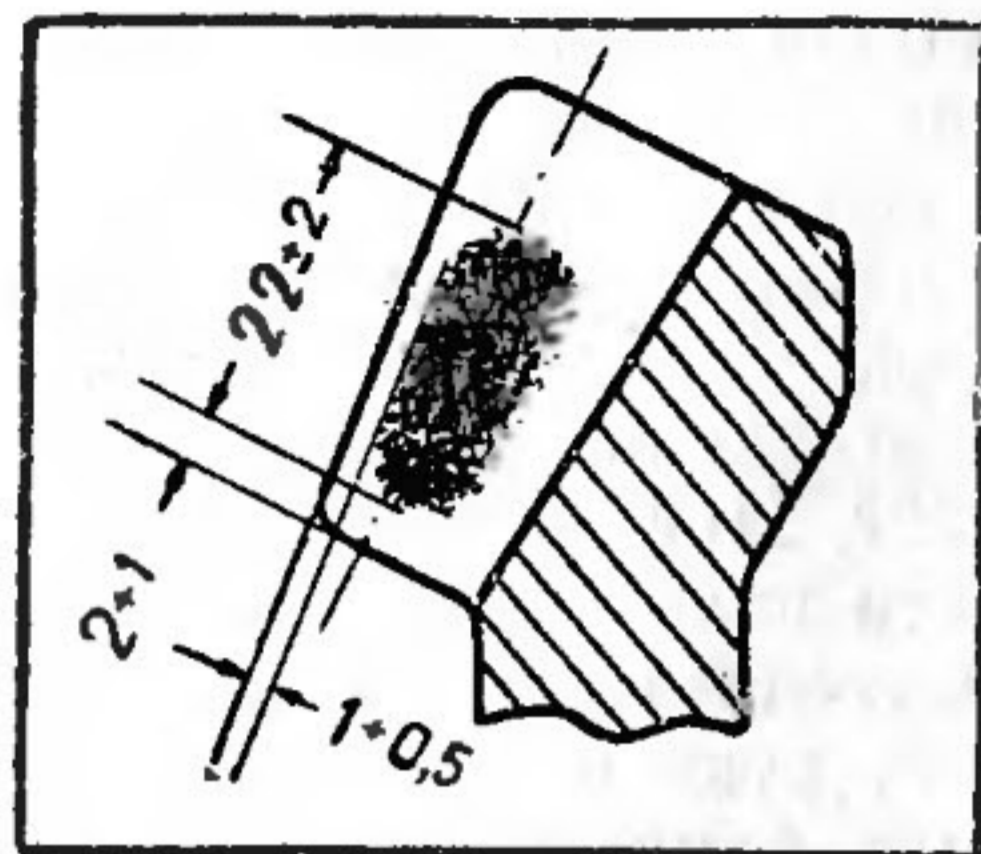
Расположение пятна контакта на зубе ведомой шестерни
